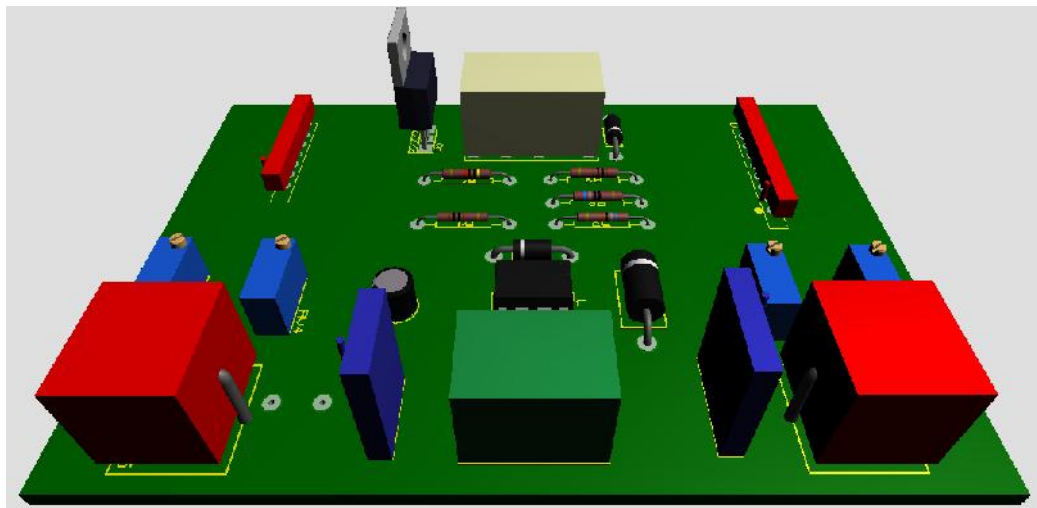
Esquema PCB diseñado en Proteus en vista 3D.
